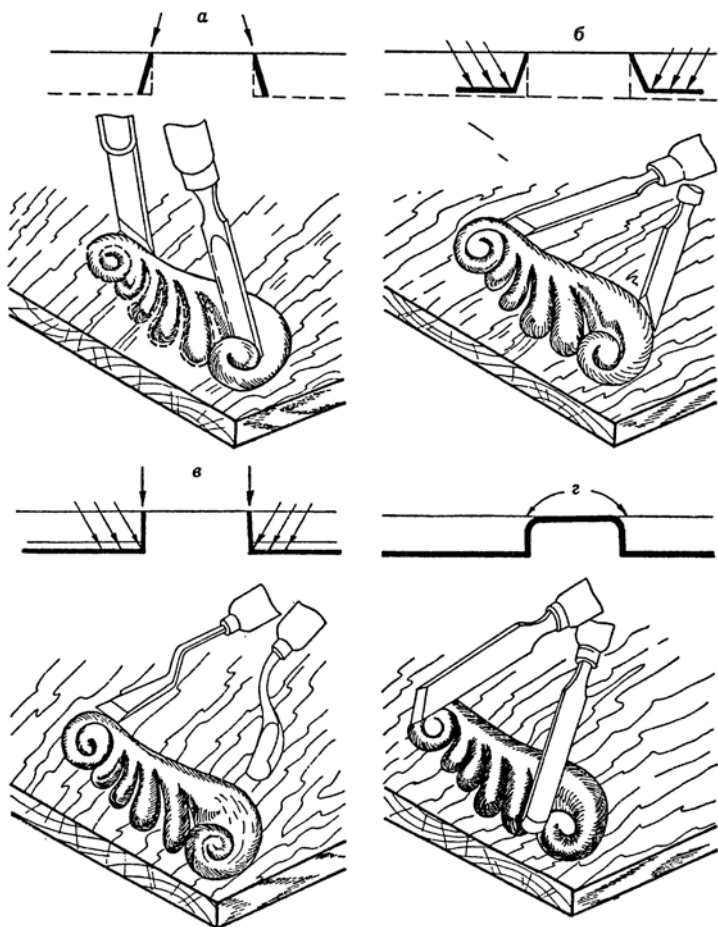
Выполнение рельефной резьбы: а — надрез; б — подрезки; в — выборка и зачистка фона и вертикального края контура; г — оваливание контура
